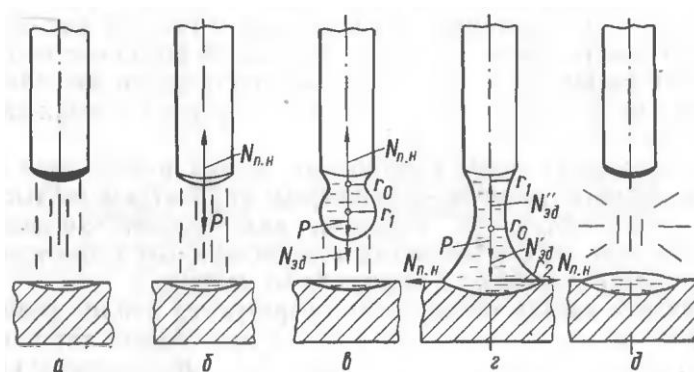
Этапы образования и переноса жидкого металла с электрода в сварочную ванну а, б – образование капли на торце электрода; в – появление шейки на стыке жидкого металла с твердым металлом электрода; г – замыкание капель дугового промежутка; д – разрыв образованного мостика и возникновение дуги.
